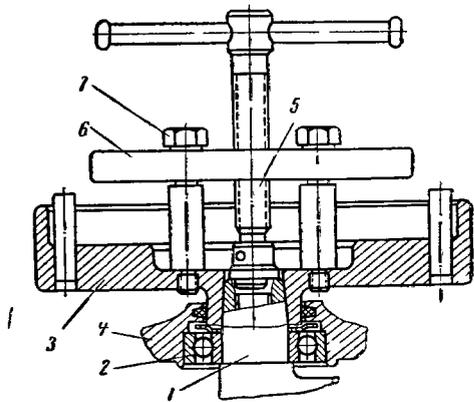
Приспособление для снятия маховика двигателя: 1—задняя цапфа кривошипа; 2—шарикоподшипник; 3—маховик; 4—задний корпус подшипника; 5—винт в сборе; 6—траверса; 7—болты для снятия маховика.
